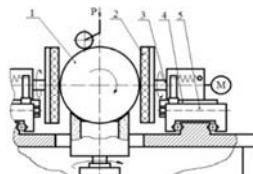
Устройство для шлифования шаров из поделочного камня
